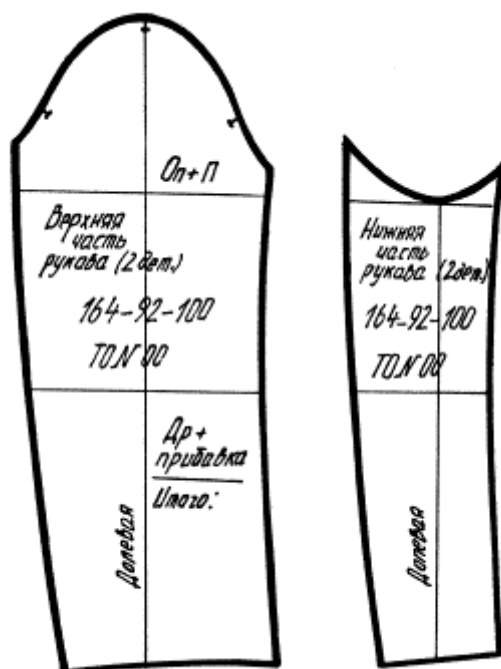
Рабочие чертежи лекал базовых конструкций
